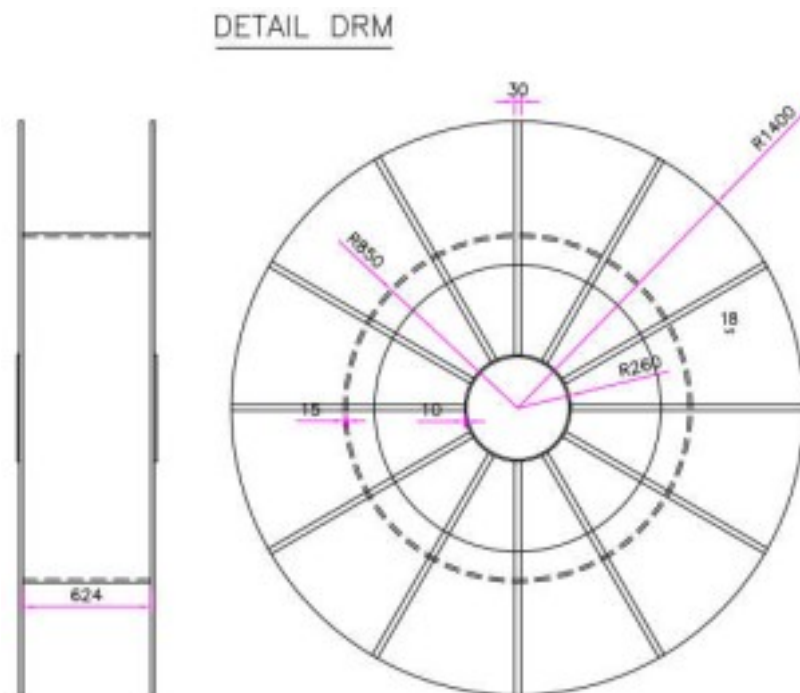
Konstruksi Pondasi *Airgun Umbilicals Winch Roller
